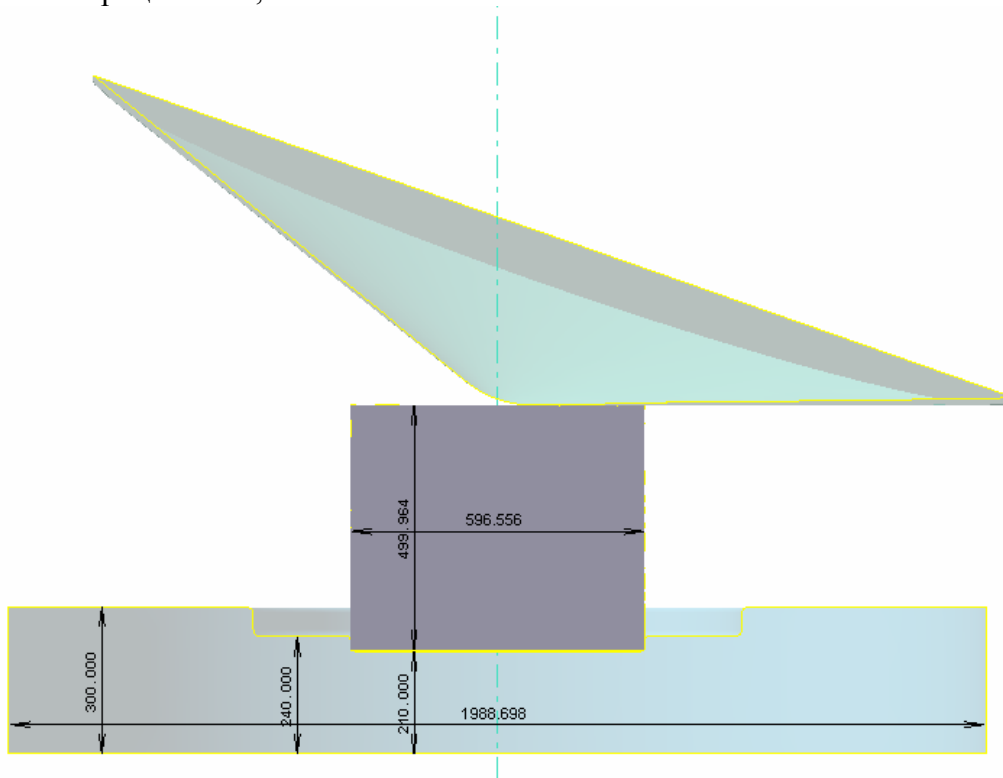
Геометрия исходной заготовки и рабочих инструментов
